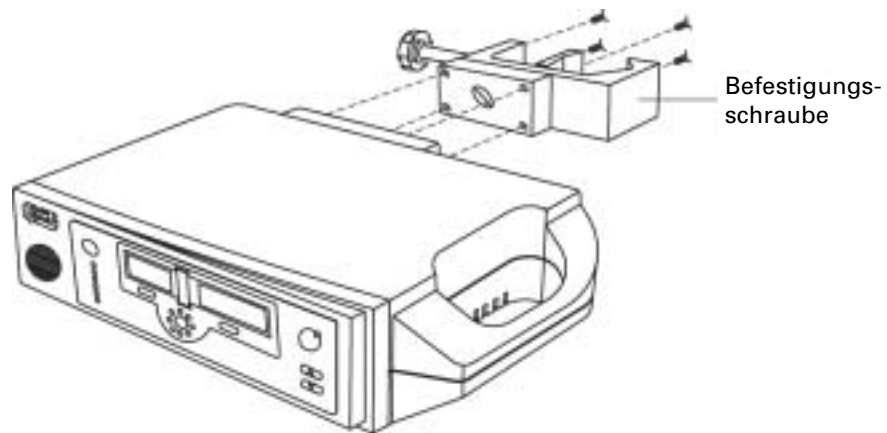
Anbringen der Befestigungsschraube für Gerätemontage
